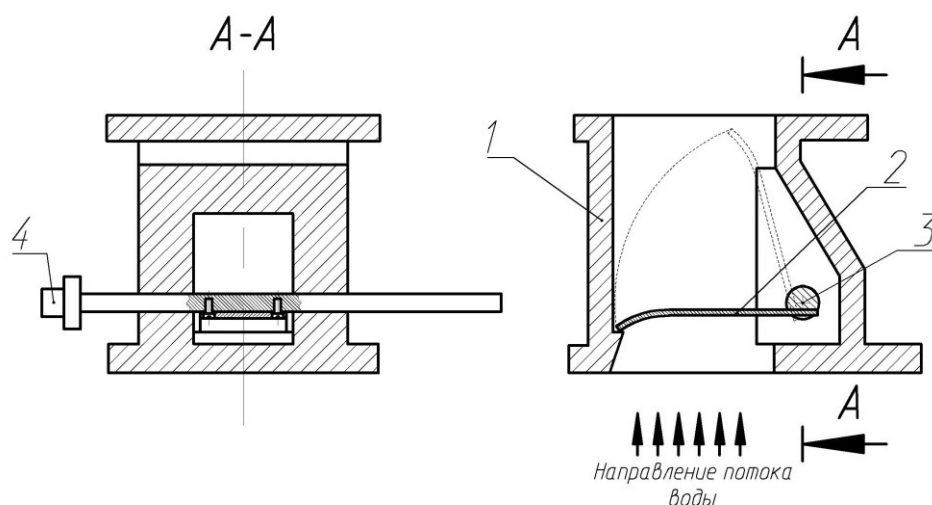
Патрубок измерительный: 1 – корпус; 2 – заслонка; 3 – ось заслонки; 4 – потенциометр.
